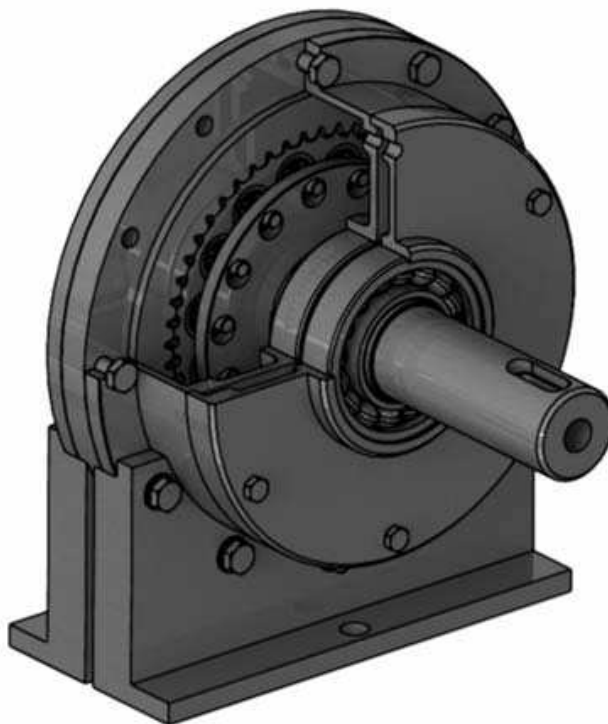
3D-модель планетарного эксцентрикового редуктора
